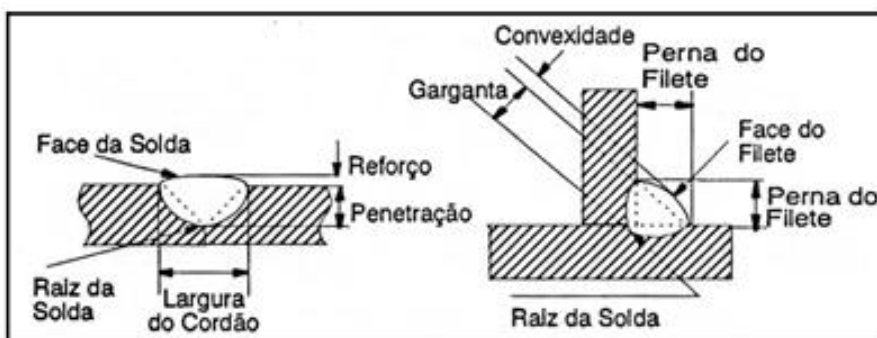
Algumas dimensões e regiões de soldas de topo e filete
